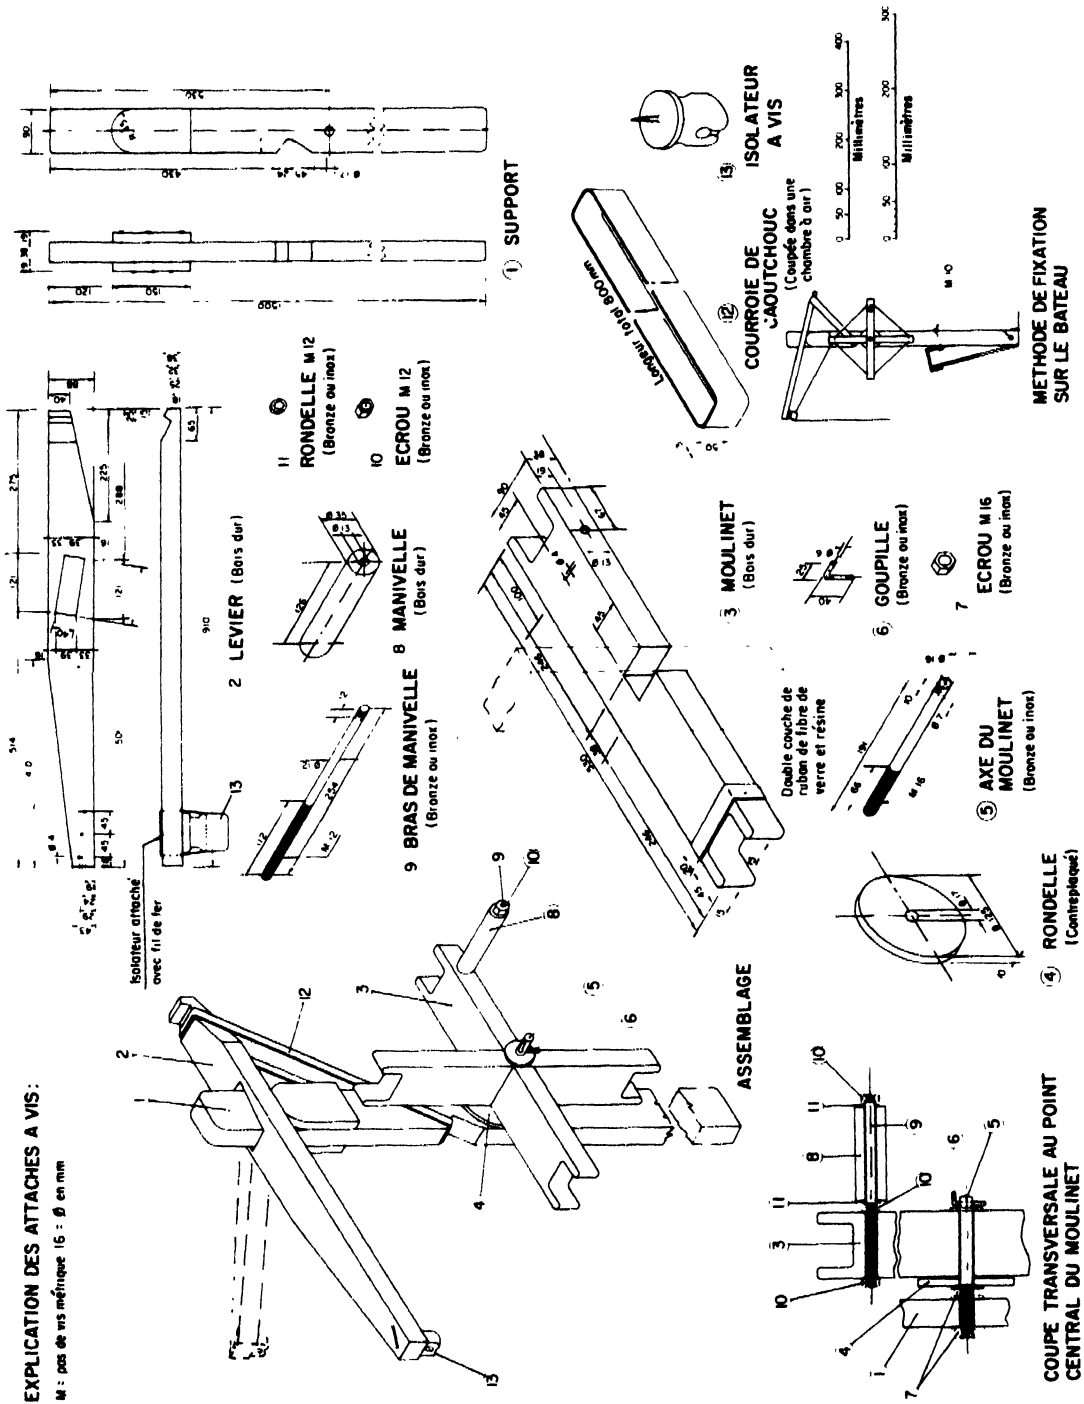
DETAILS DE CONSTRUCTION D'UN MOULINET A MAIN MONTE SUR BOSSOIR
